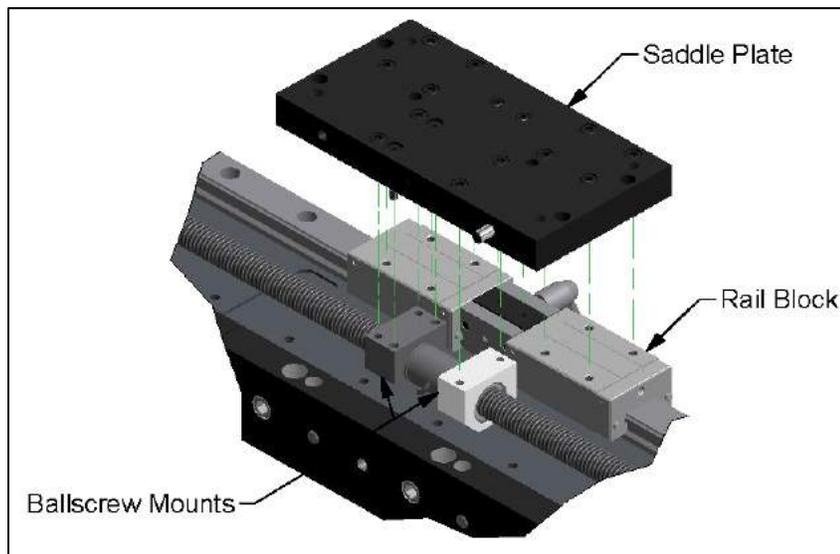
Montajes de tornillo de bola (izquierda) y placa de sillín (arriba) y bloqueo de riel (derecha)
